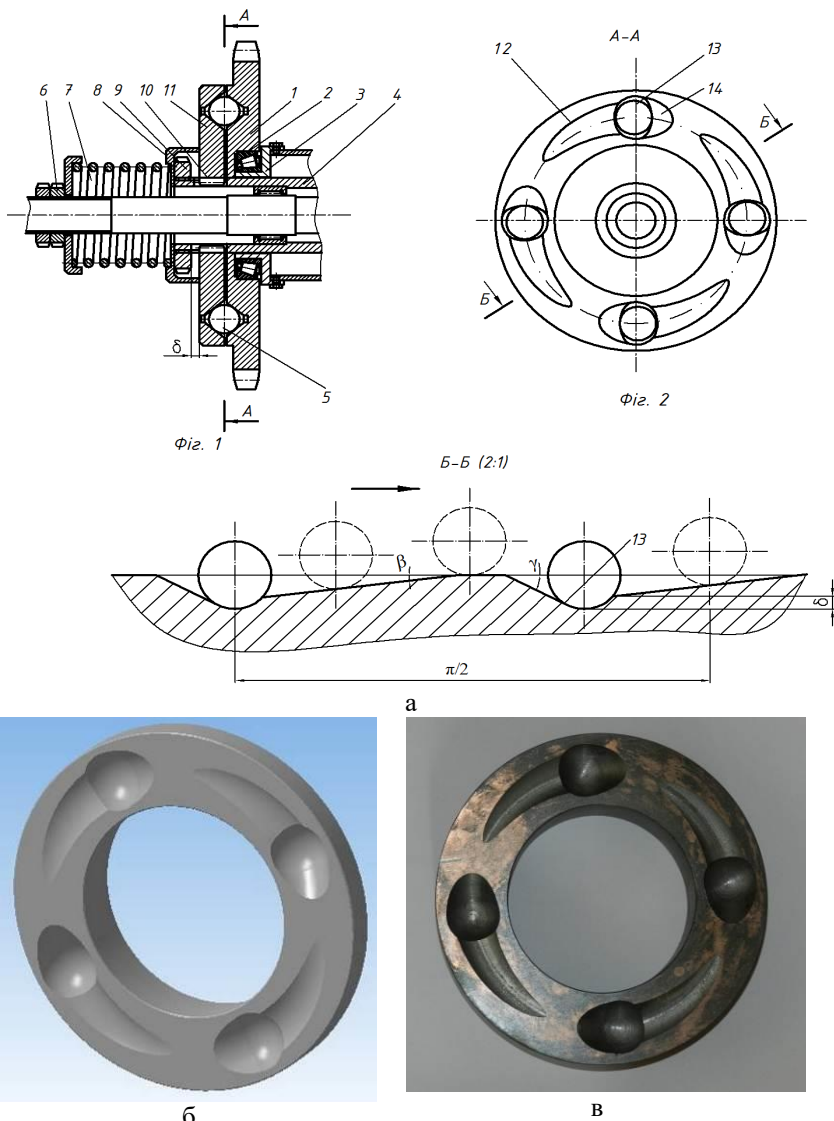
Конструктивна схема запобіжного пристрою (а) та загальний вигляд робочі поверхні ведучої півмуфти: б – модель, виконана в КОМПАС 3D; в – загальний вигляд виготовленої півмуфти
